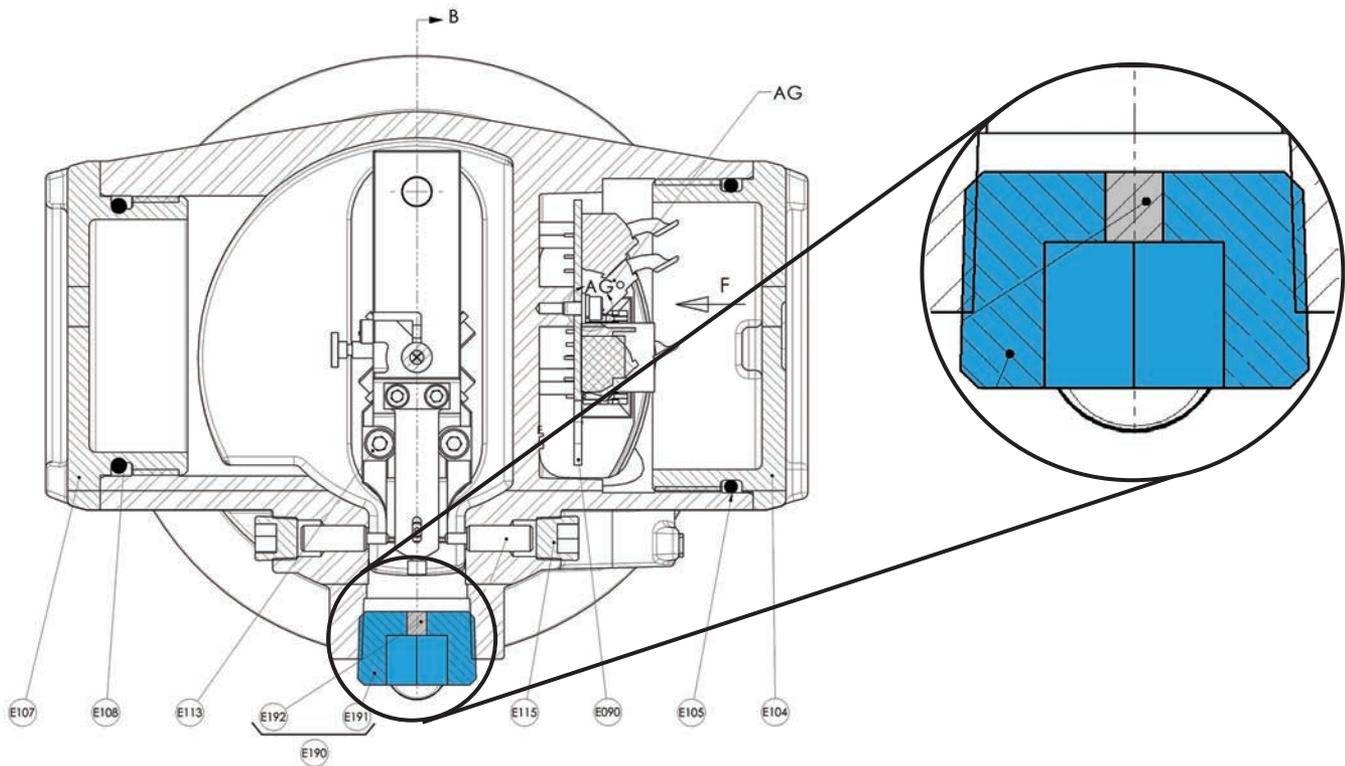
Vista posterior del DLT 12400 en sección transversal de la caja
